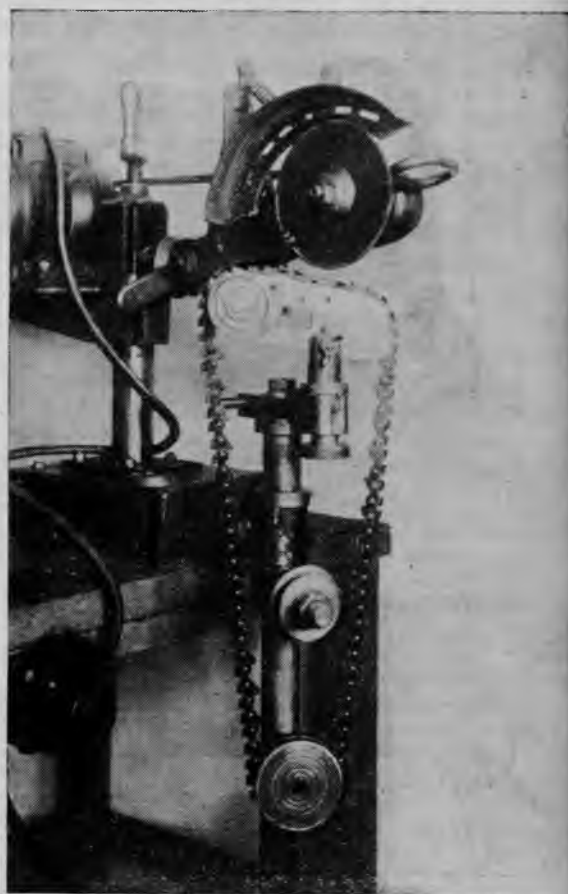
Станок Витковского-Елисеева с прибором ЦНИИМЭ
